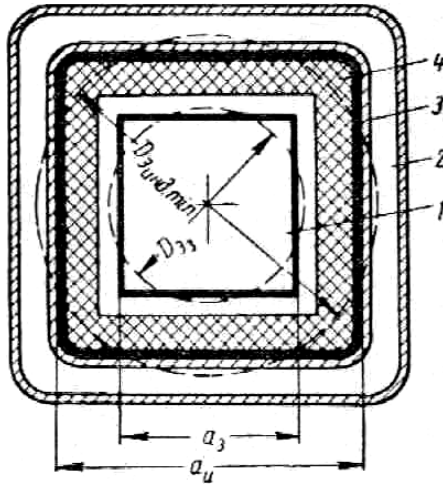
Вид поперечного сечения индуктора, предназначенного для нагрева заготовок квадратного сечения:
